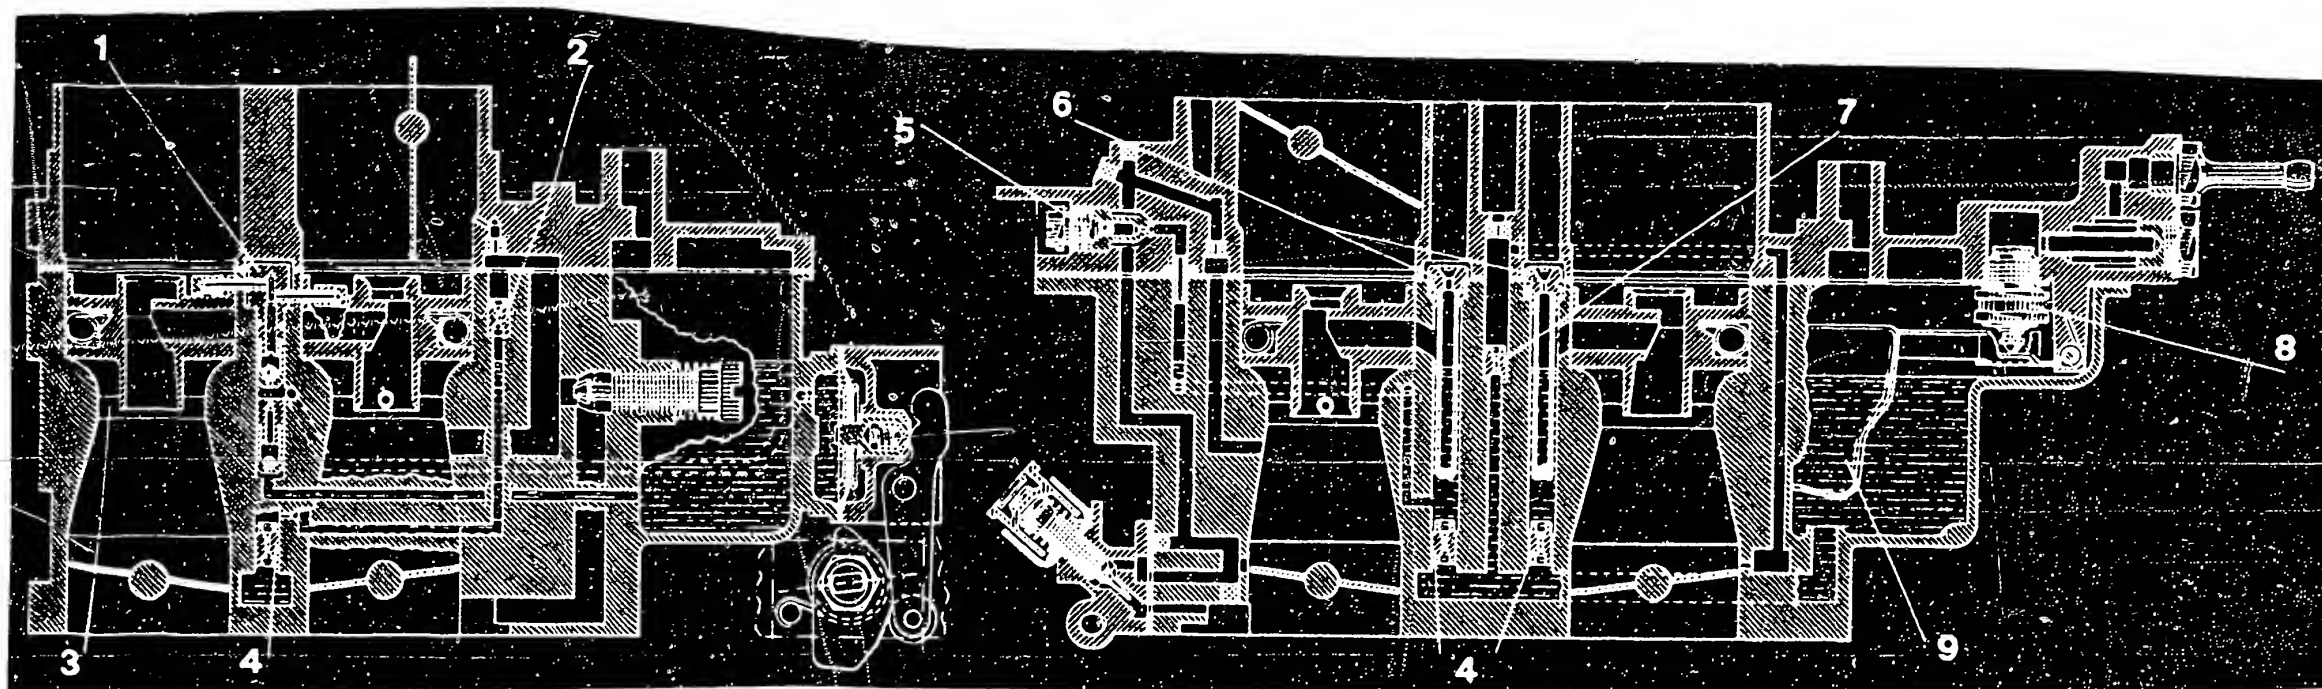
Schnittzeichnung des Solex 32/35 TACIC: 1 Einspritzrohr – 2 CO-Einstellschraube – 3 Lufttrichter – 4 Hauptdüse – 5 Leerlaufdüse – 6 Luftkorrek-
